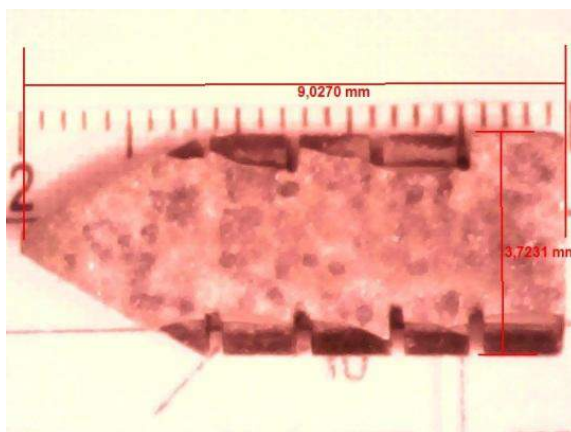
Загальний вид руйнування консольних міні-балочок на верхній різальній поверхні твердосплавної пластини ВКЗ
